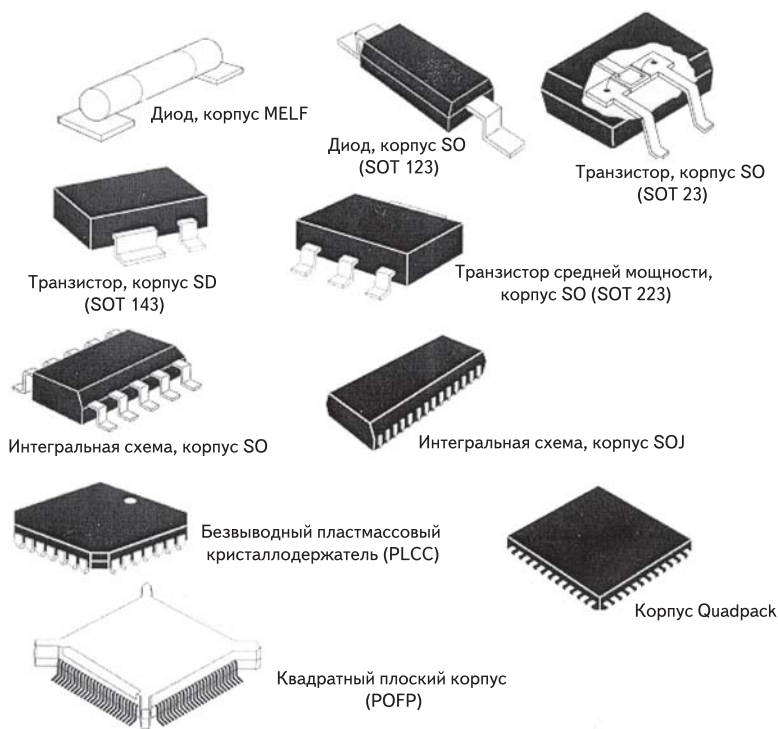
Конструкции типовых корпусов полупроводниковых компонентов поверхностного монтажа
